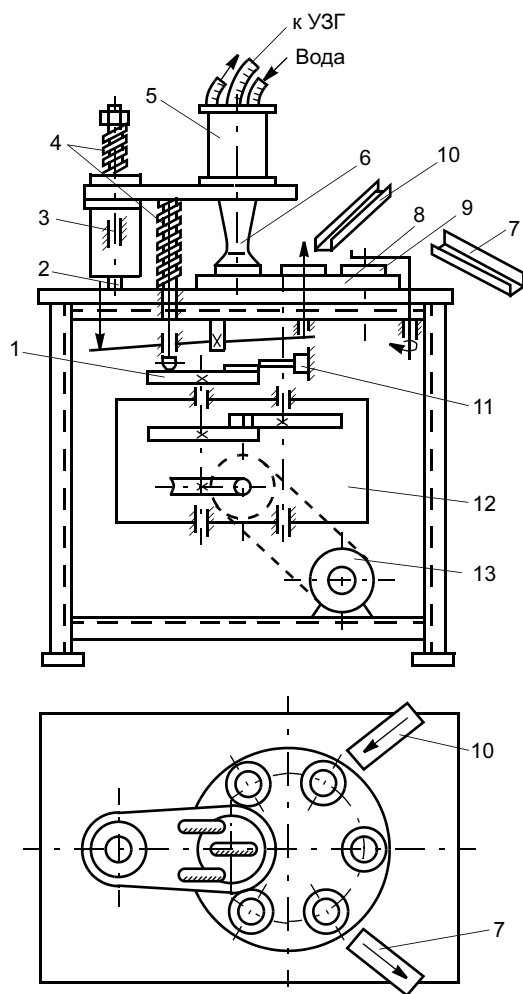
Схема работы ультразвуковой сварочной установки УПК-15М1
